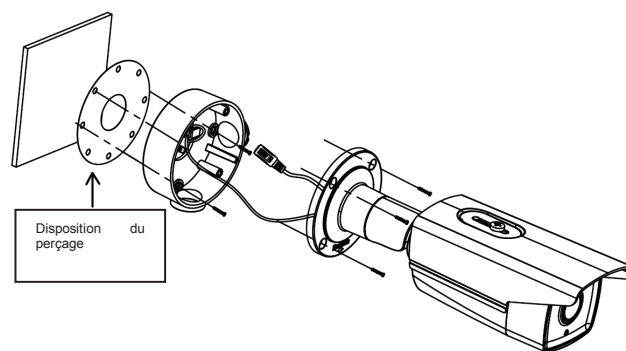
Installation de la caméra sur le mur à l'aide d'une base de montage
